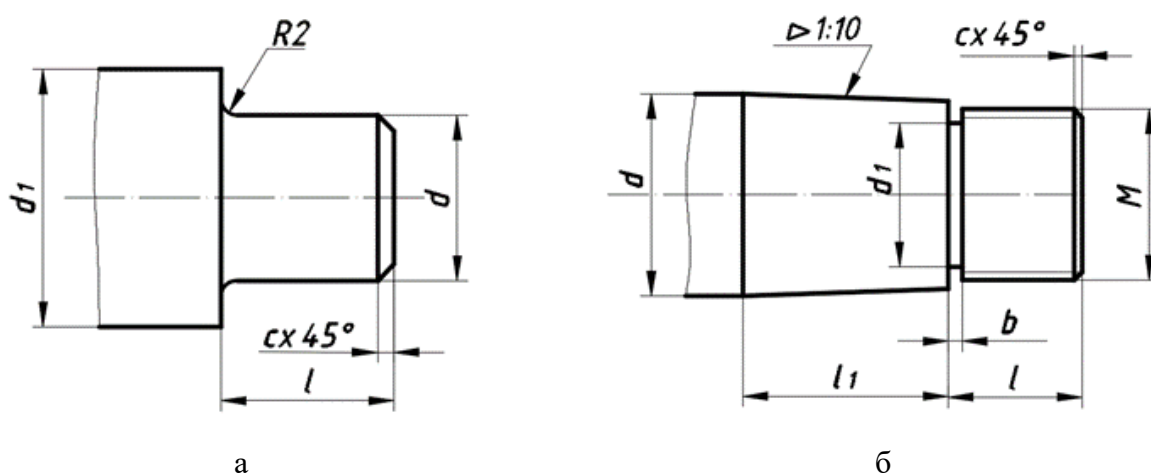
Образец выполнения чертежа детали типа «Вал».
